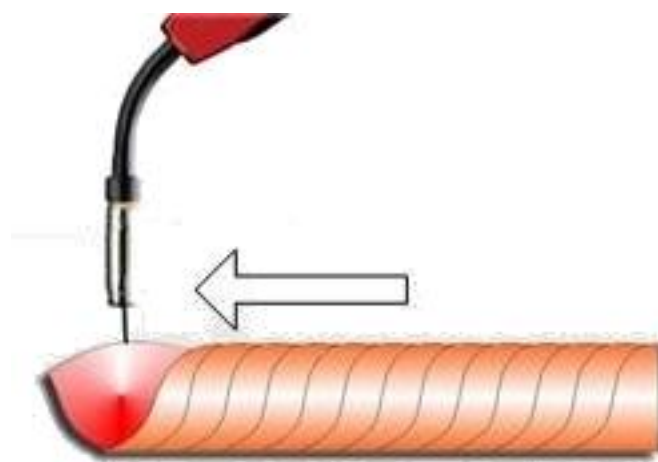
Схема процесса механизированной сварки при перпендикулярном положении оси ввода проволоки в сварочную ванну
